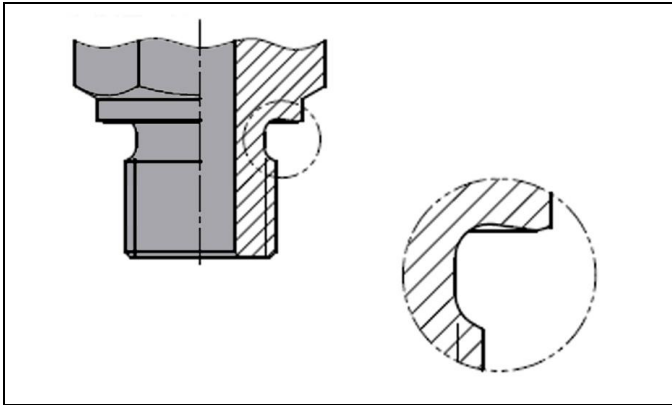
Einschraubzapfen mit Dichtkante (Form B)
